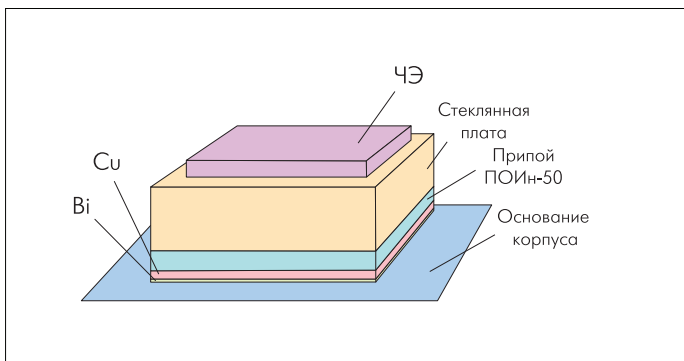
Схема расположения деталей при посадке чипа на основание корпуса с помощью припоя
